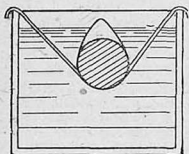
Ванна для наплавки кулачков распределительного вала и калки их
